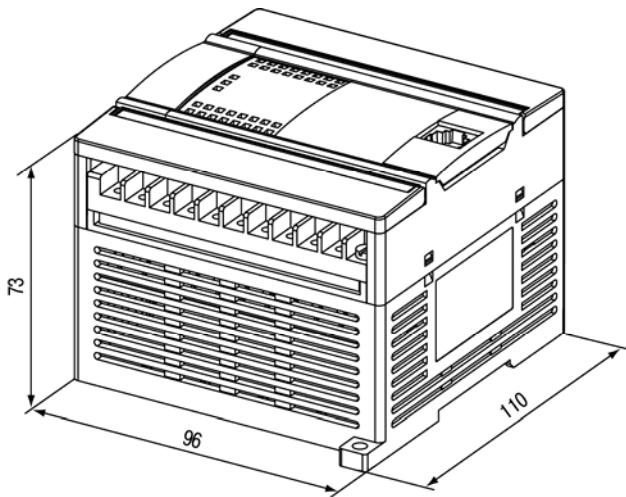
Габаритный чертеж ПР110-х.12х.8х
